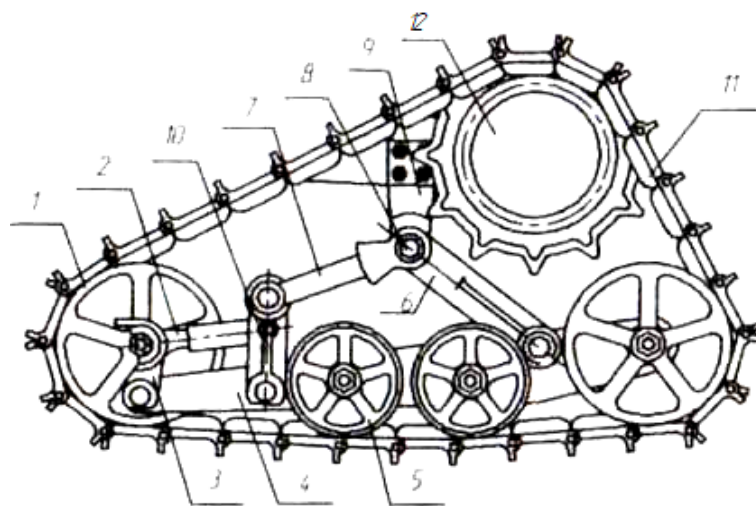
Полугусеничный движитель с жёстко закрепленными опорными катками
